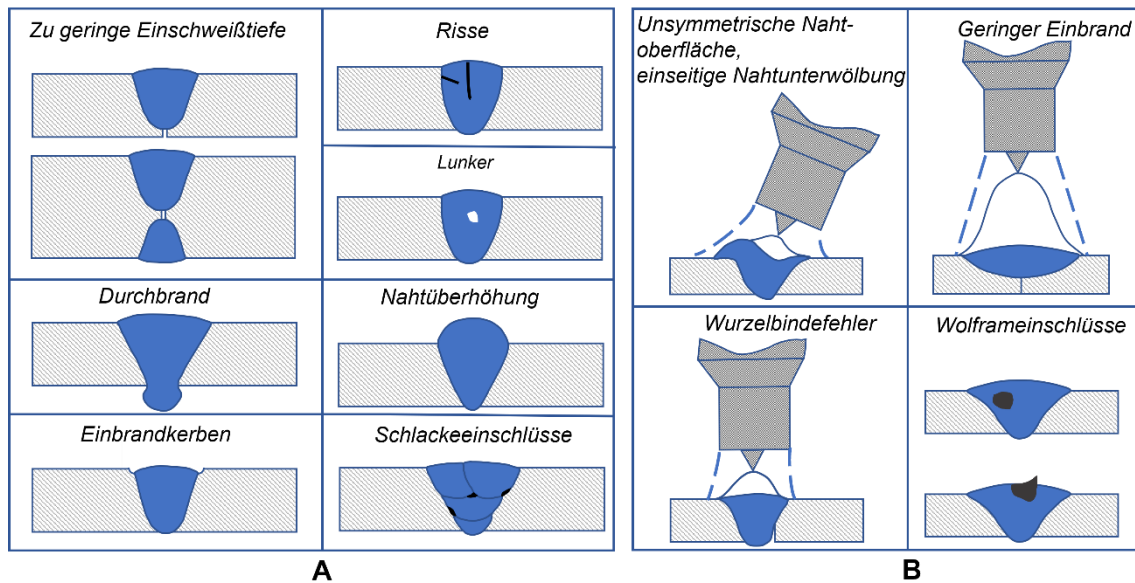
A: Beispiele für Fehler beim UP-Schweißen, B: Beispiele für Fehler durch Brennerführung beim WIG-Schweißen, nach /KUS 22/
